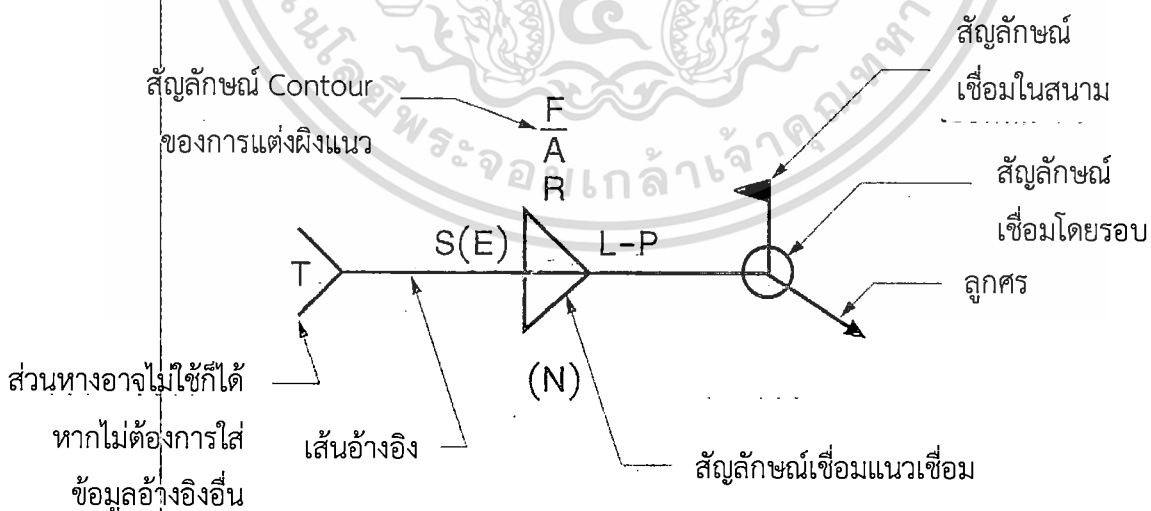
แสดงแนวเชื่อมฟิลเล็ต (Fillet weld)
